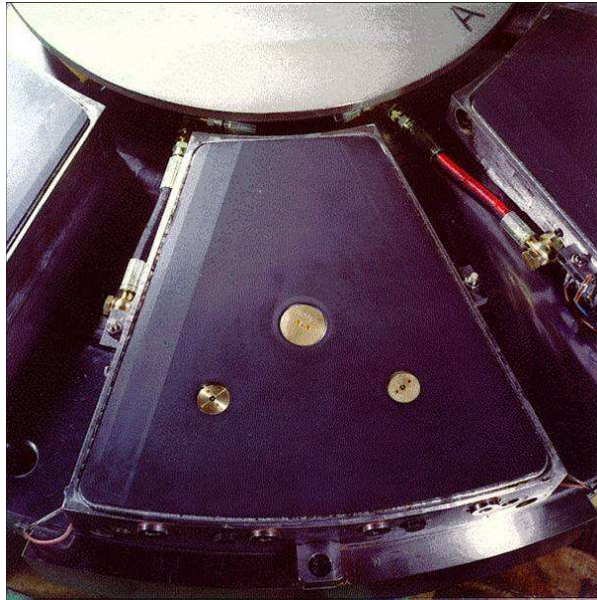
Opatřovaná kluzná vrstva na bázi cínu [8] Obr. 3.9: PTFE segment po 1500 hodinách provozu ve stejném stroji [8]
